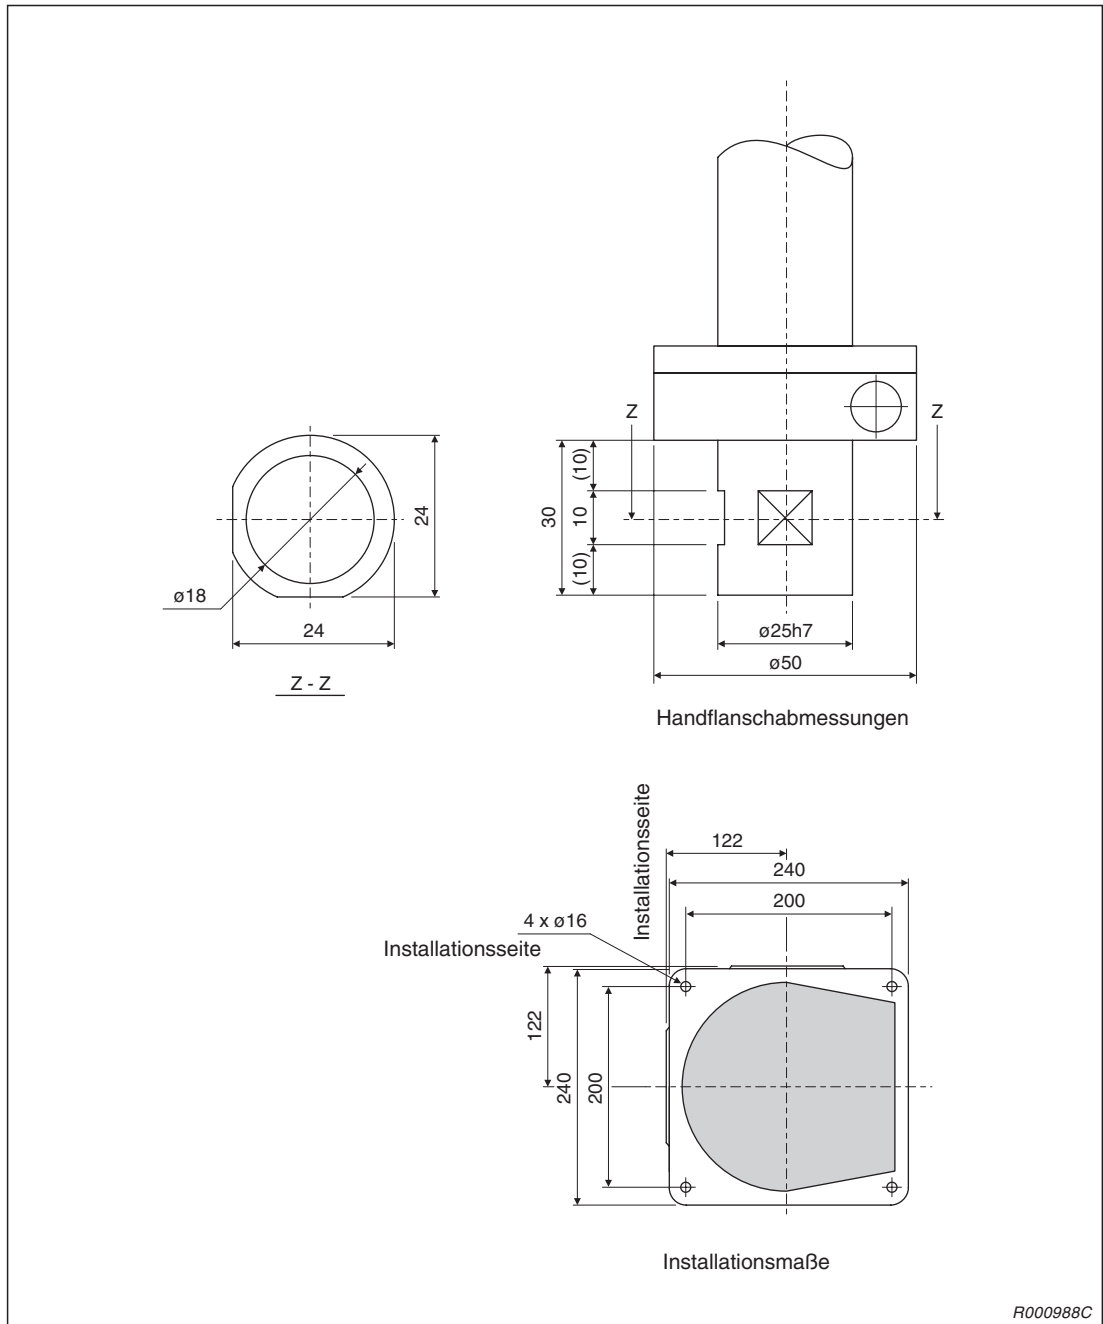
Handflanschabmessungen und Installationsmaße der Roboter RH-12SH
